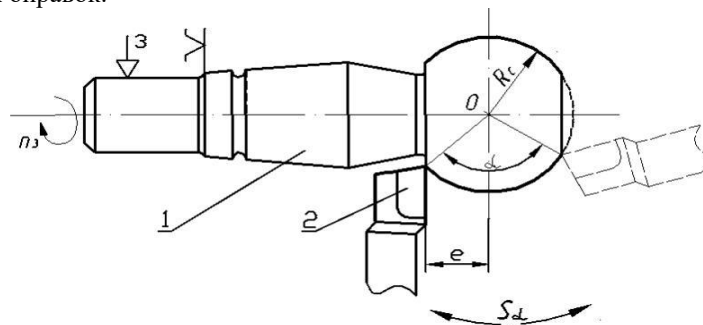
Кінематична схема обробки неповної сферичної поверхні кульового пальця:
